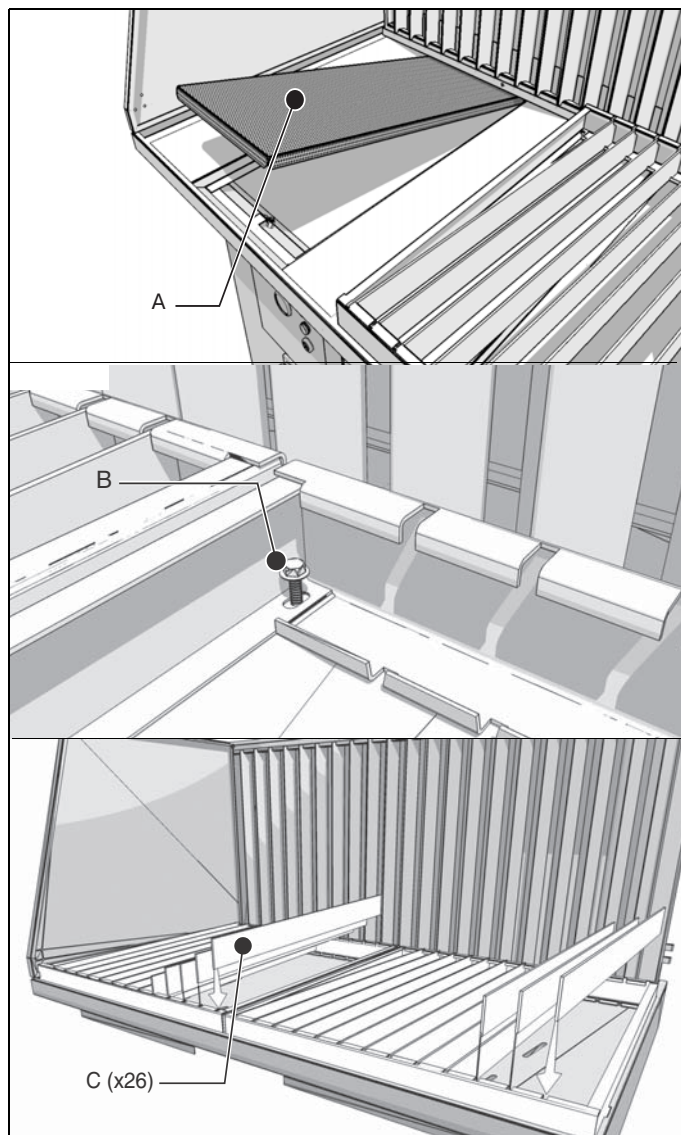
Montage de la grille de travail pour découpe plasma
